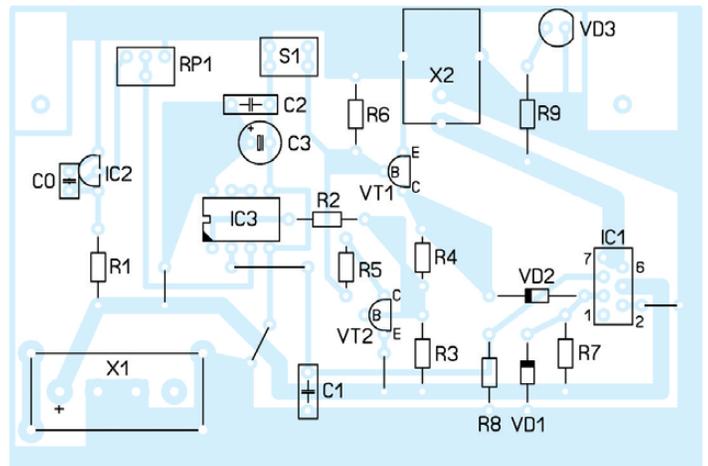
Bestückung der Leiterplatte für die Schutzschaltung 3; IC1 ist wiederum stehend einzulöten.
